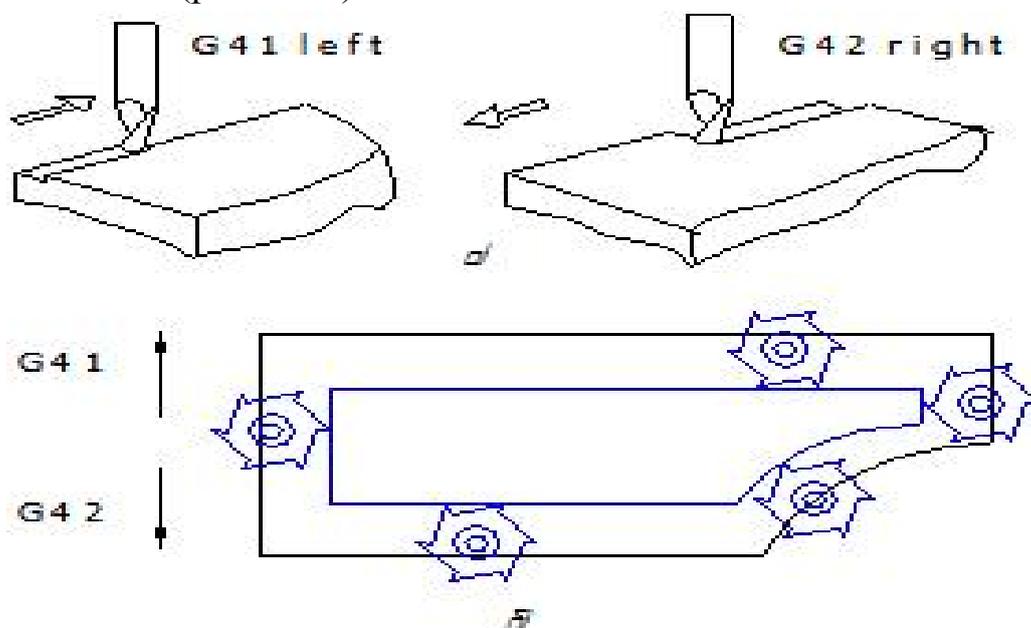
Схема обработки, поясняющая выбор направления коррекции на радиус фрезы при обработке: а – прямолинейного контура, б – криволинейного контура
